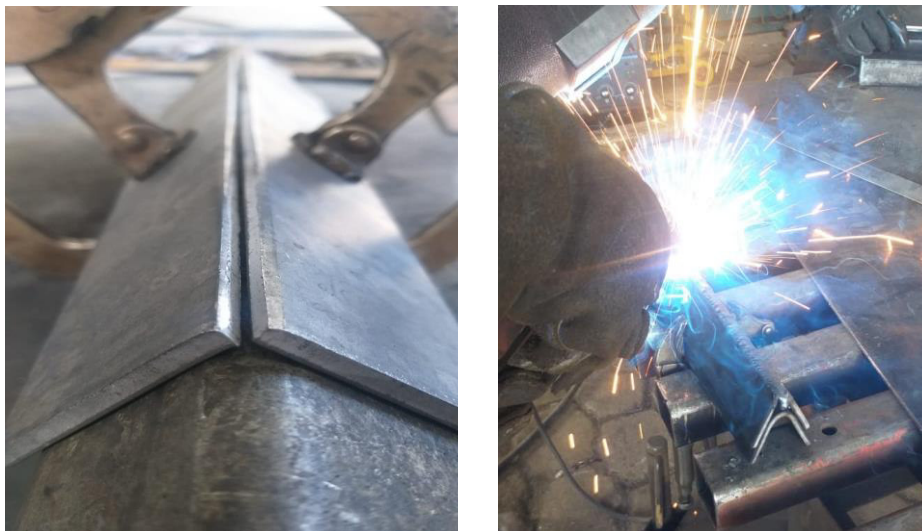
Posición de soldadura para obtención de perfiles angulares.
